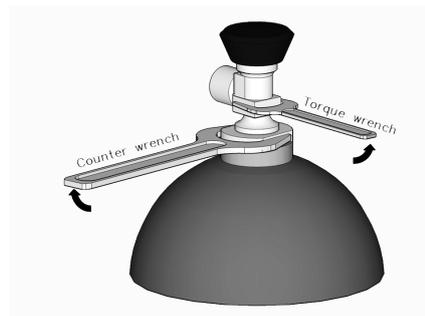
Verwendung des Gegenschlüssels für die Demontage des Ventils
